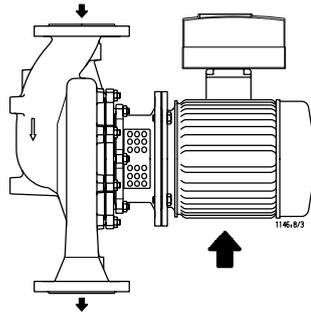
Horizontaler Einbau Pumpenaggregat mit PumpDrive, Durchflussrichtung von oben nach unten
